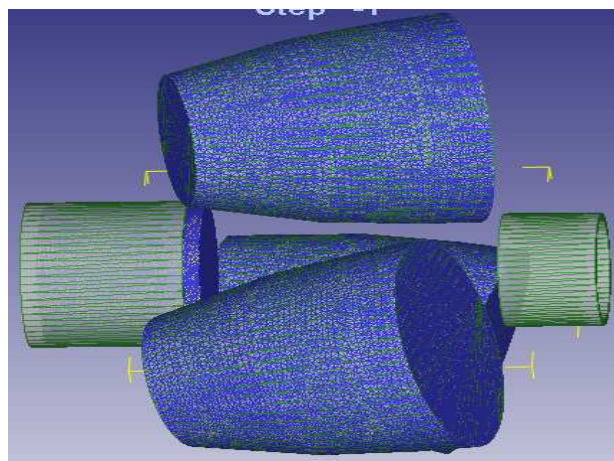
Сборка в Deform-3D поперечно-винтовой прокатки
